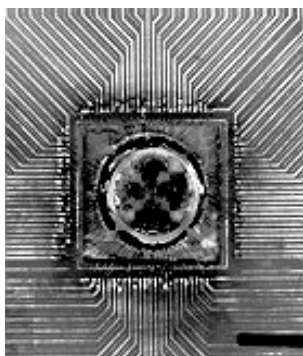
Vista superior da matriz soldada à placa de circuito impresso com trilhas para acesso aos eletrodos.
